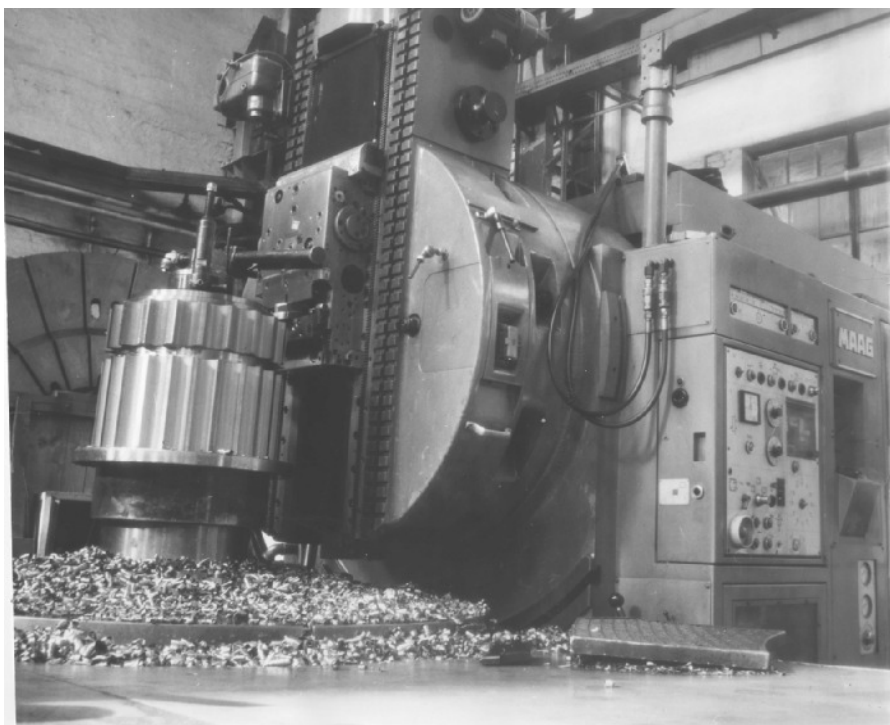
Нарезка круговых зубьев на зубострогальном станка МААG SH 450/500
